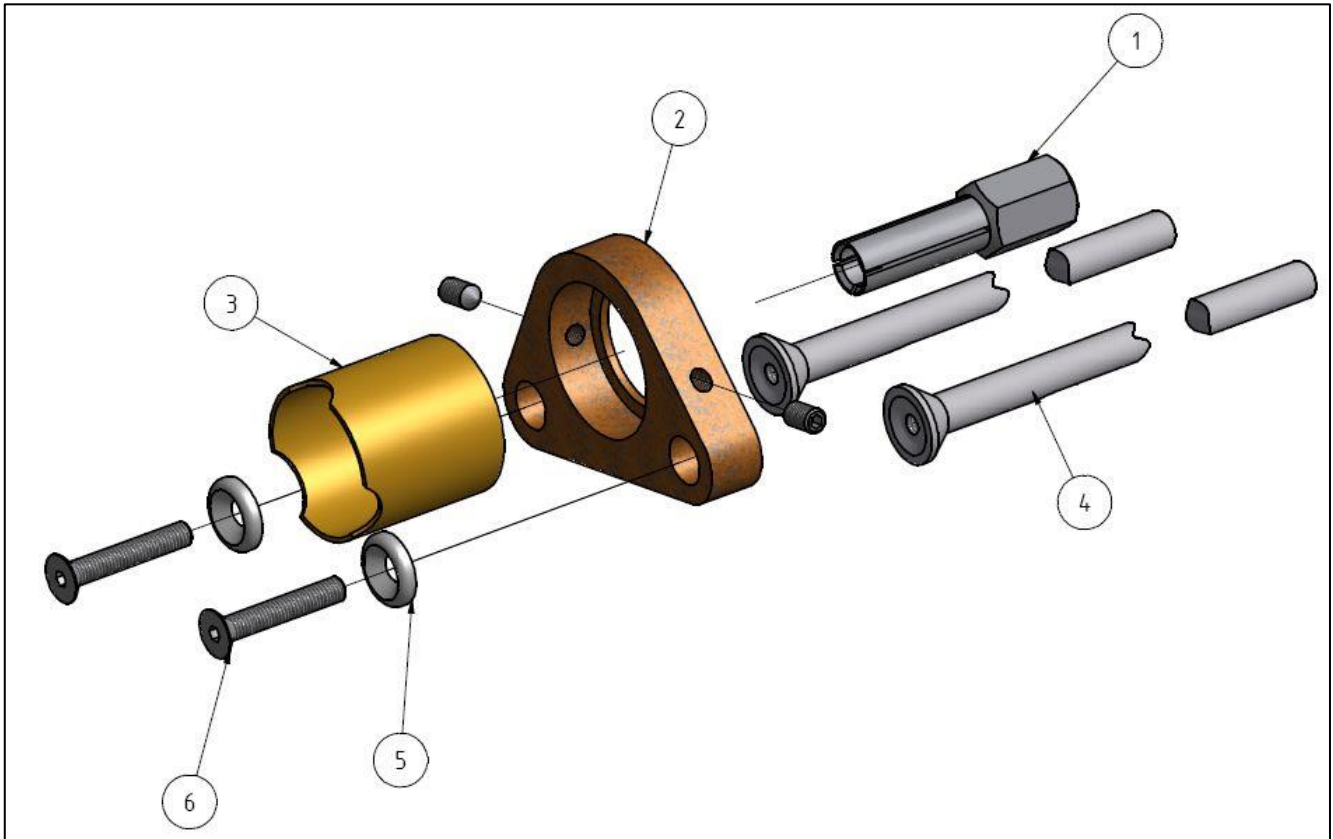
Stützeinrichtung zum Kurzzeitbolzenschweißen ohne Schutzgas
